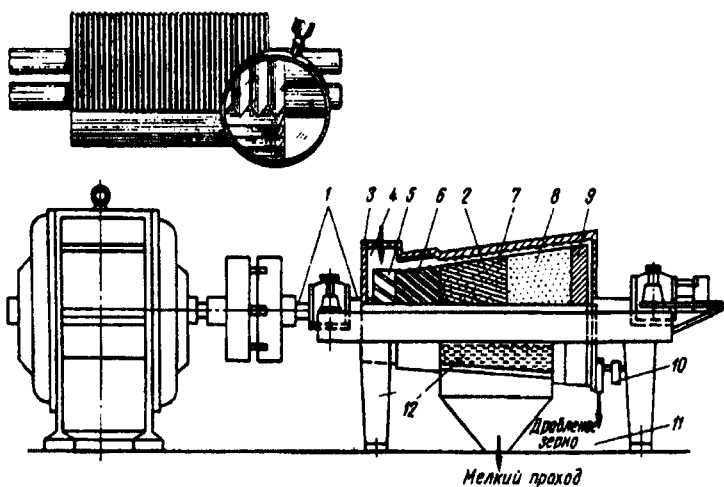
Схема дежерминатора для дробления зерна кукурузы:
